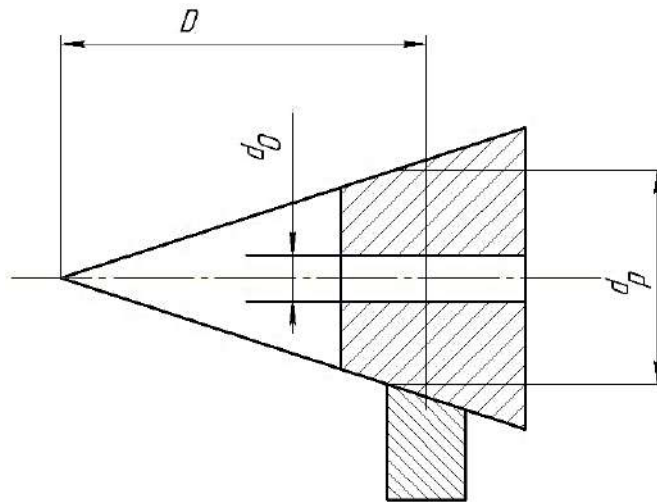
Схема кругової опорної рейки поворотного візка
